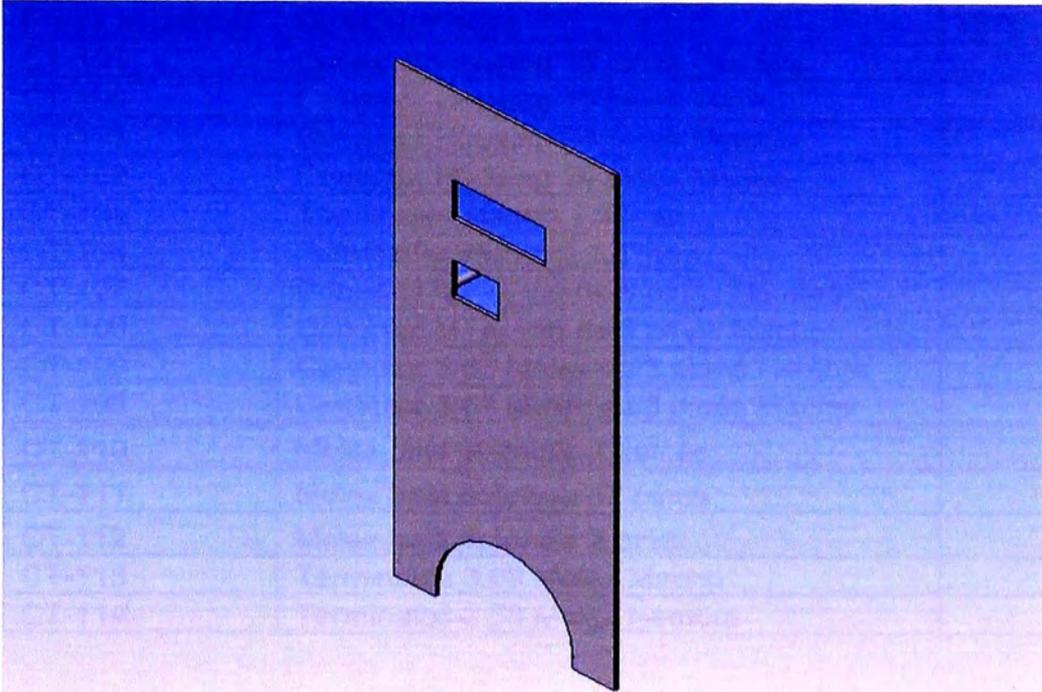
Modelo de Careta del producto en Solidworks, donde la tarjeta electrónica es montada.
